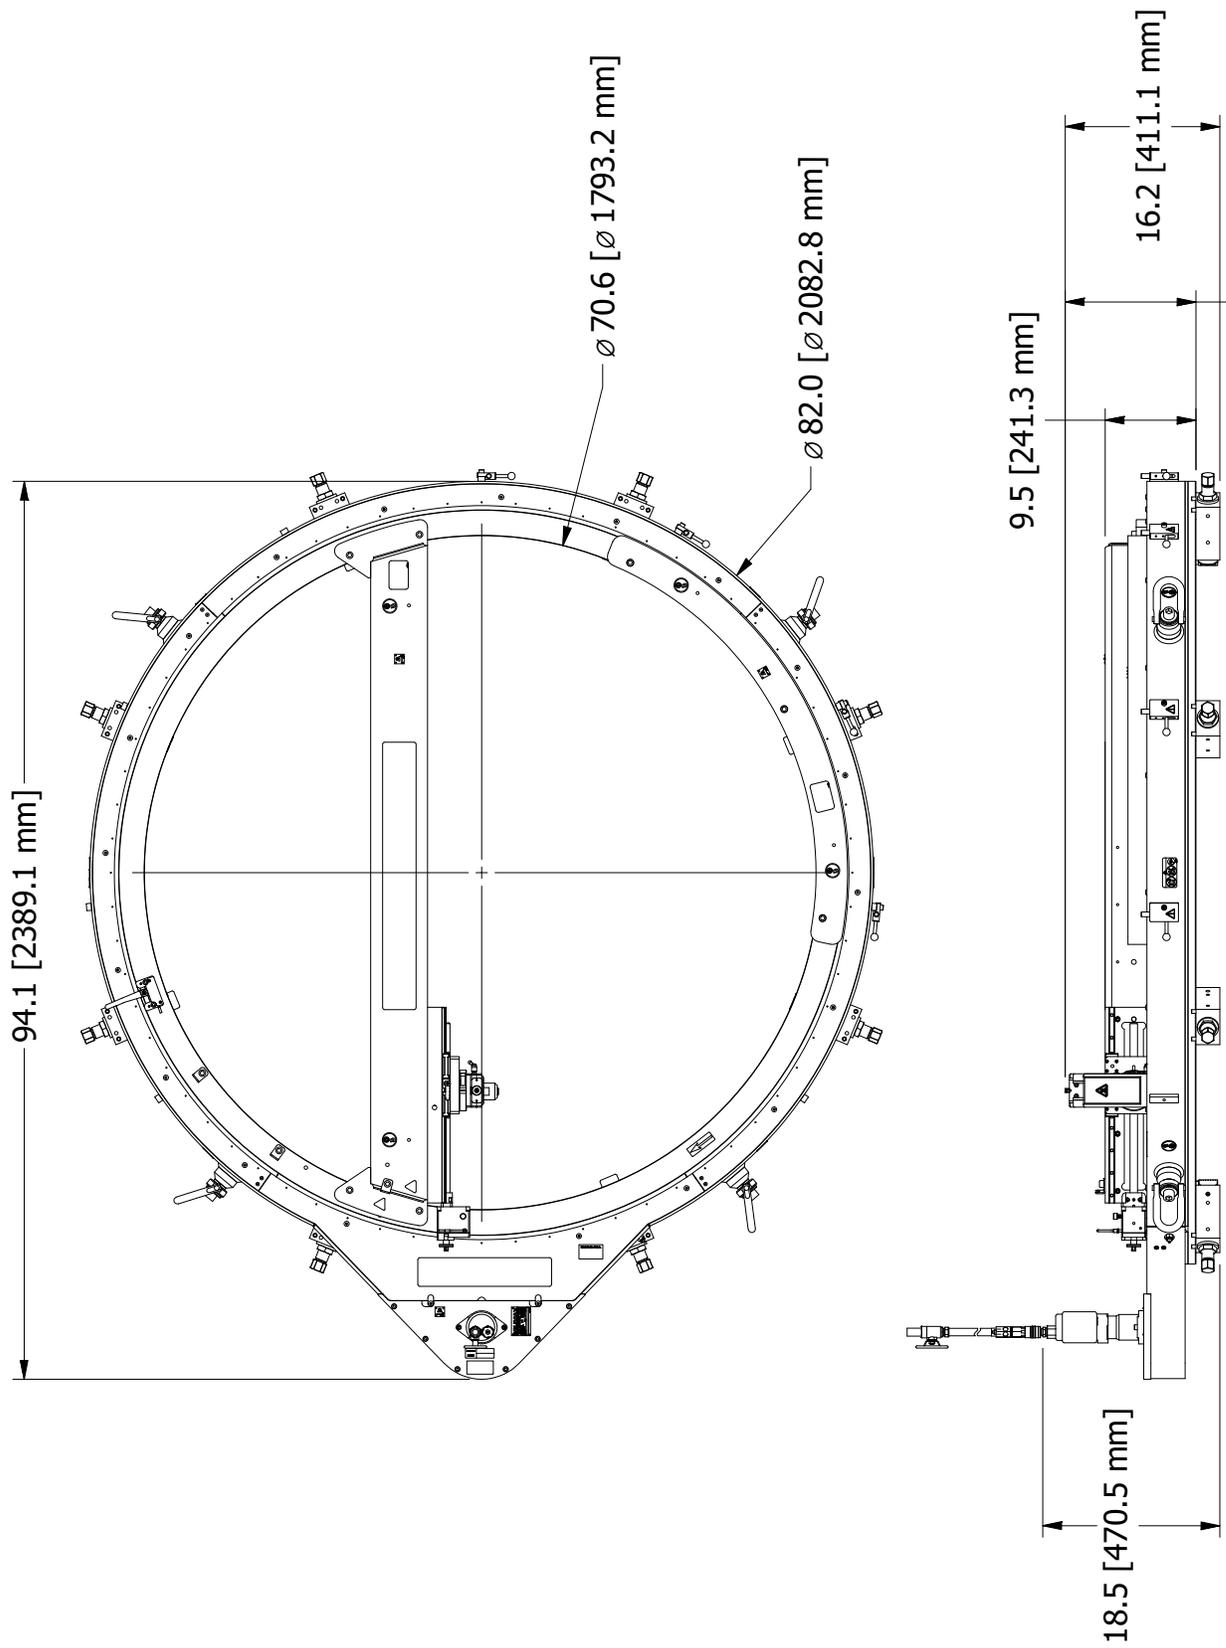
DIMENSIONS DE LA SURFACEUSE RAPIDE ODF70 SPEED FACER (REF. 87000)
